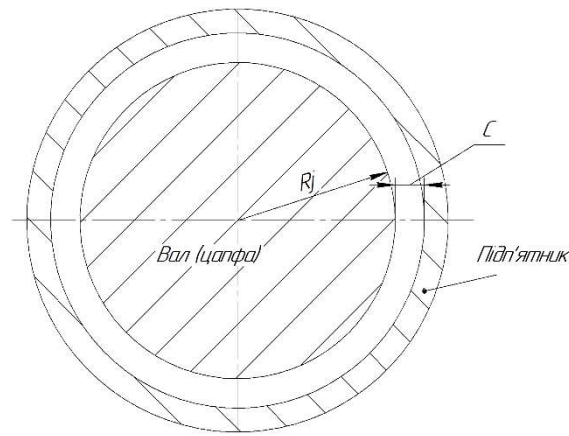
Схема гідродинамічного циліндричного підшипника ковзання
